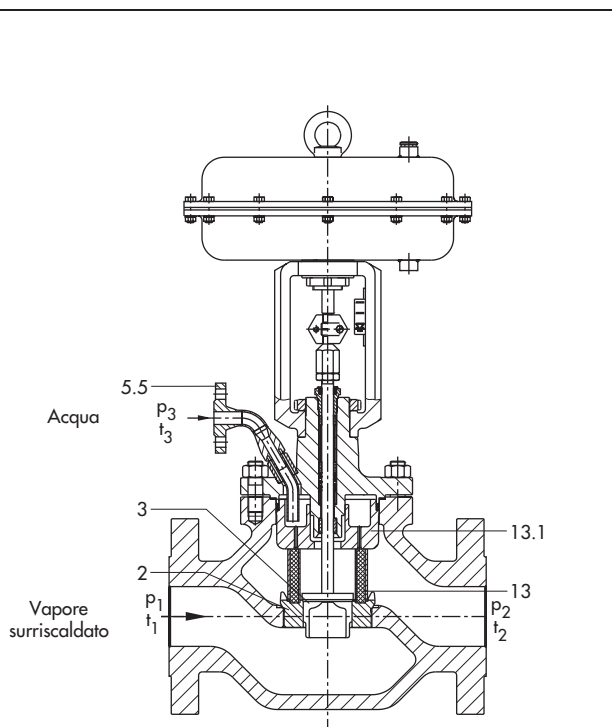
· Desurriscaldatore pneumatico Tipo 3281-1 con attacchi flangiati e attuatore Tipo 3271
